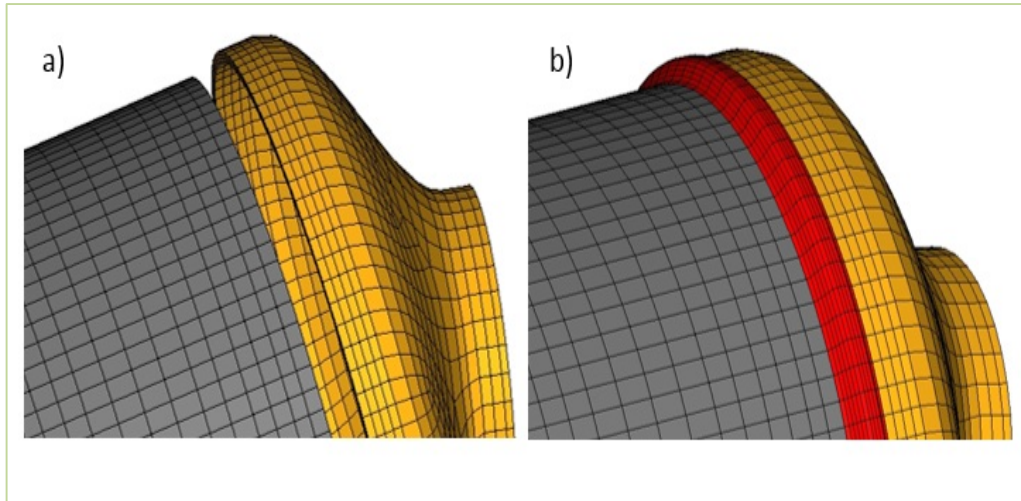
SOLDADURA ENTRE LOS COMPONENTES CARCASA (GRIS) Y CONO (AMARILLO). A) COMPONENTES SIN SOLDADURA DONDE NO HAY UNIÓN ENTRE ELLOS. B) SOLDADURA (ELEMENTOS EN COLOR ROJO) EN EL ESPACIO VACÍO ENTRE CARCASA Y CONO.
